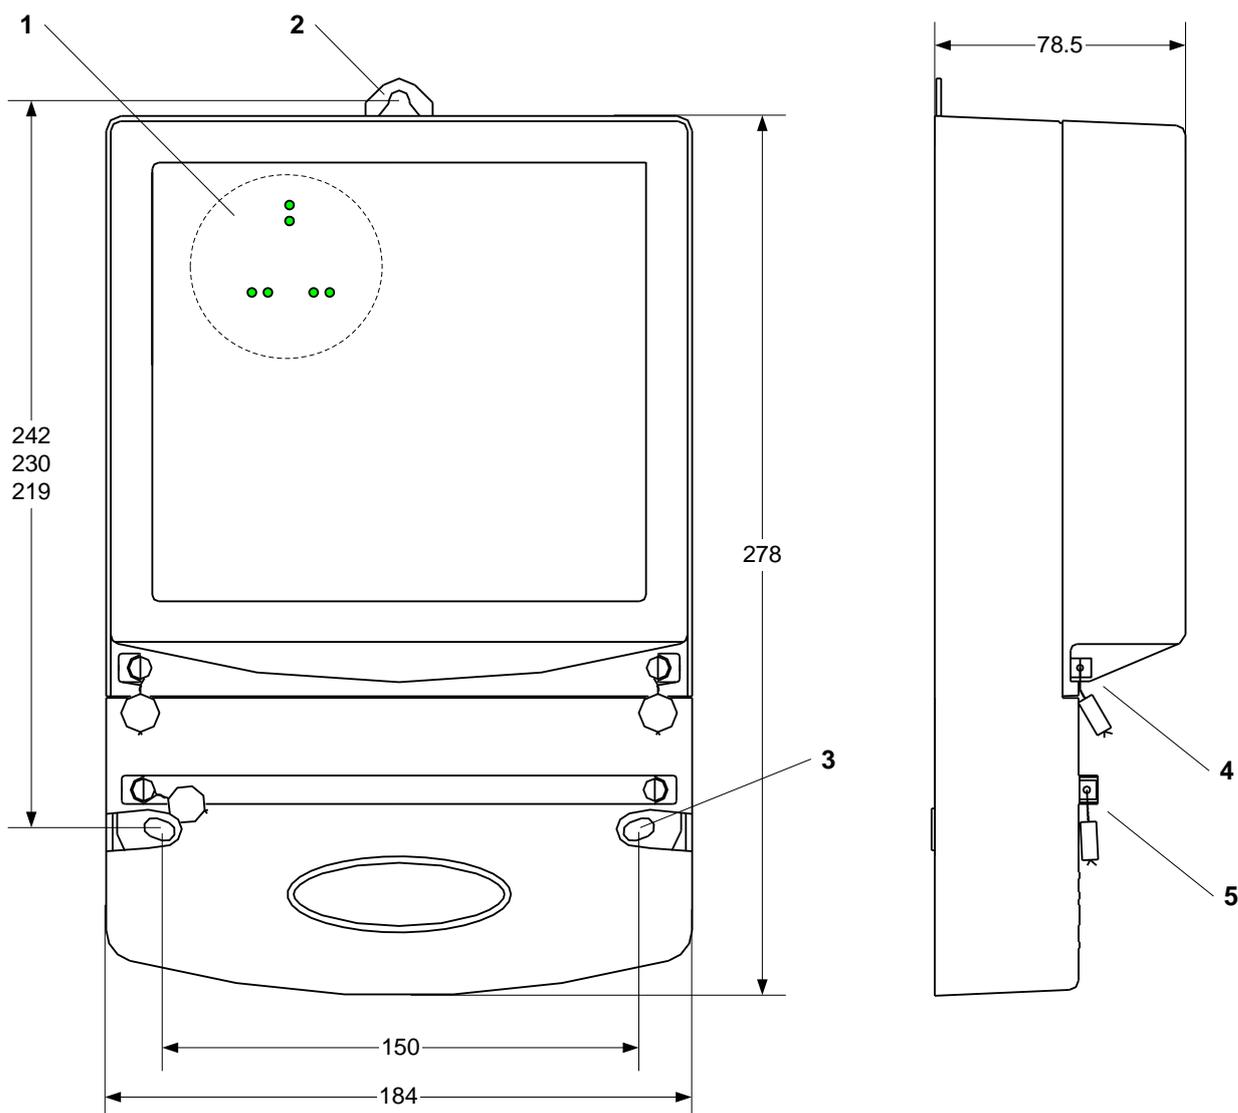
Внешний вид, габаритные и установочные размеры маршрутизатора RTR51
